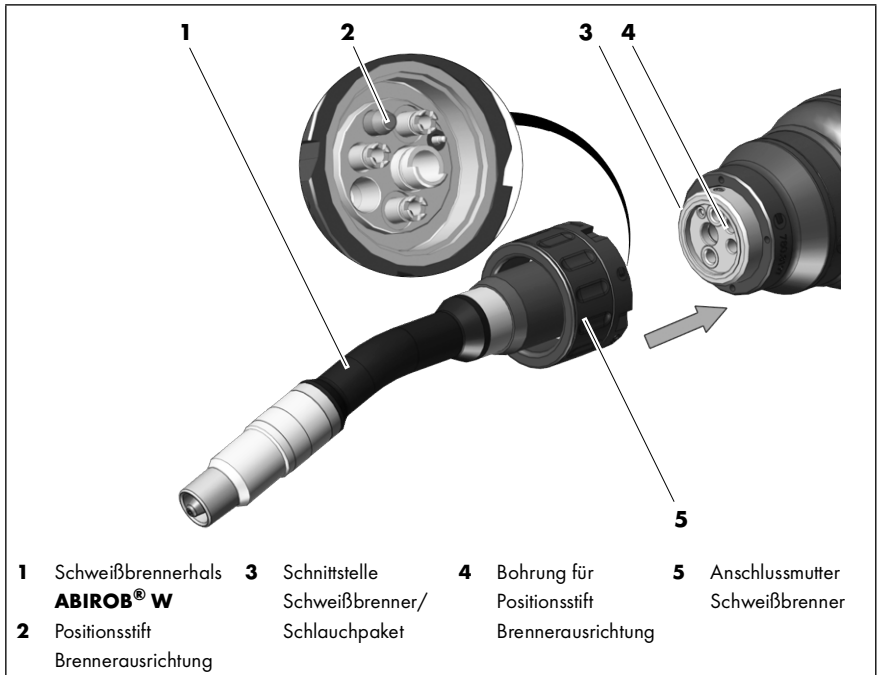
Schweißbrennerhals ABIROB® W befestigen
